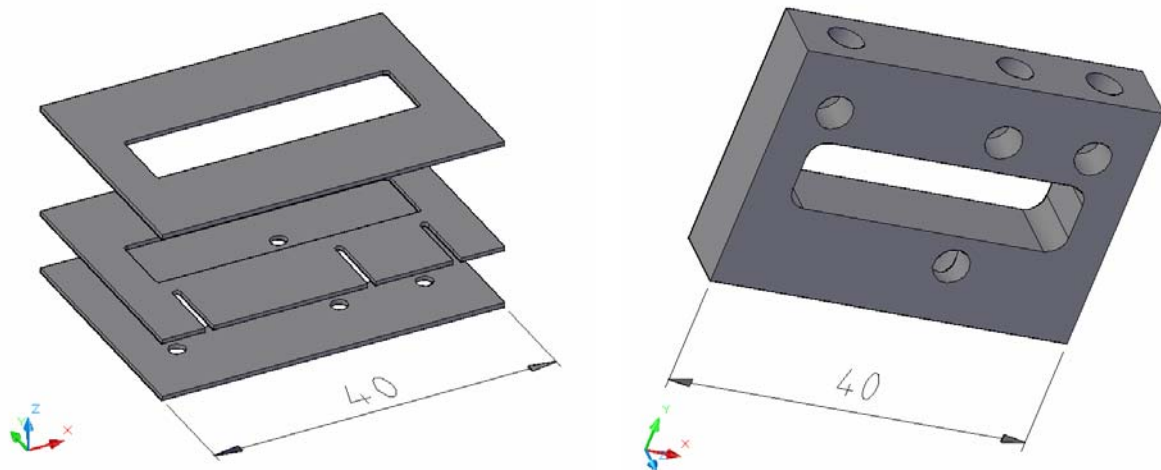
Adapter zur fluidischen Kontaktierung der Kanalstruktur Layout-K4. Links: Adapter-A4/S zum Anschluss einer Spritzenpumpe. Aufbau des Adapters in drei Einzelschichten. Abmessung $28 \times 40 \text{ mm}^2$, Gesamthöhe 1,5 mm. Rechts: Adapter A4/F zum Anschluss des Fluigent-Aktorsystems, Ansicht von unten. Abmessung $28 \times 40 \text{ mm}^2$, Höhe 8 mm.
